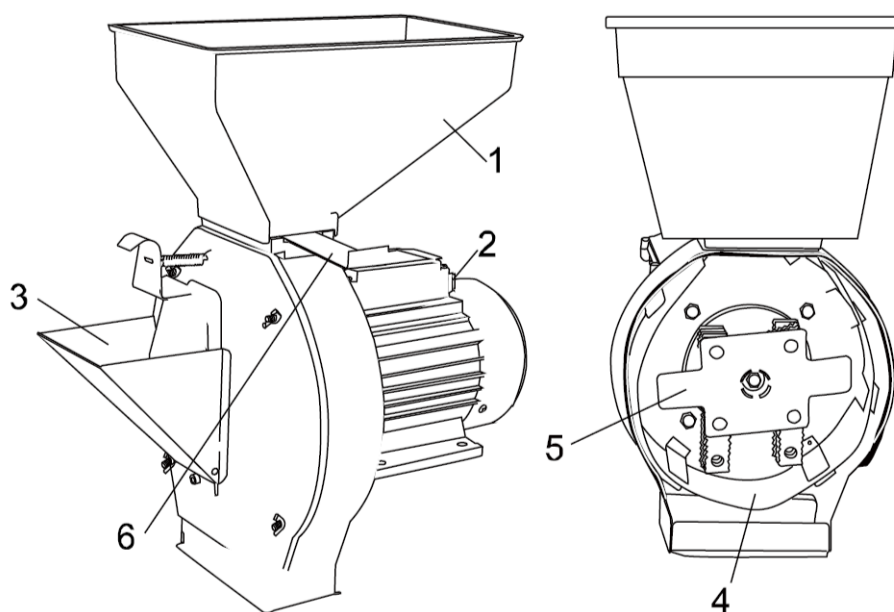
Устройство кормоизмельчителя HM2501 Sturm: 1 – бункер для загрузки зерна; 2 – кнопка выключателя; 3 – отверстие для выхода корма; 4 – сито; 5 – нож-молоток; 6 – заслонка
